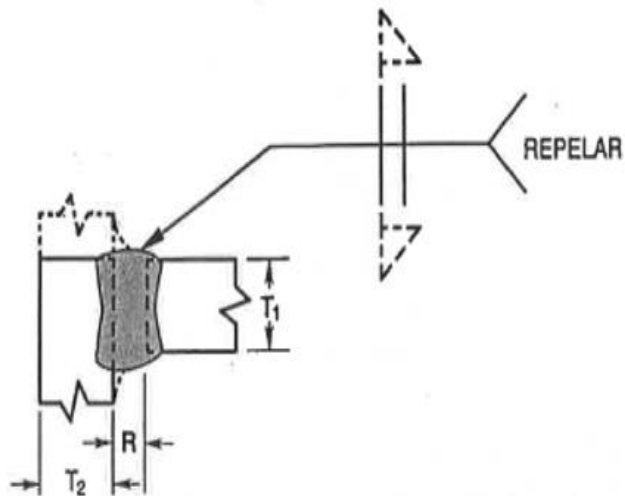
Diseño de juntas soldadas hasta 6 mm de espesor. Fuente: [15]
